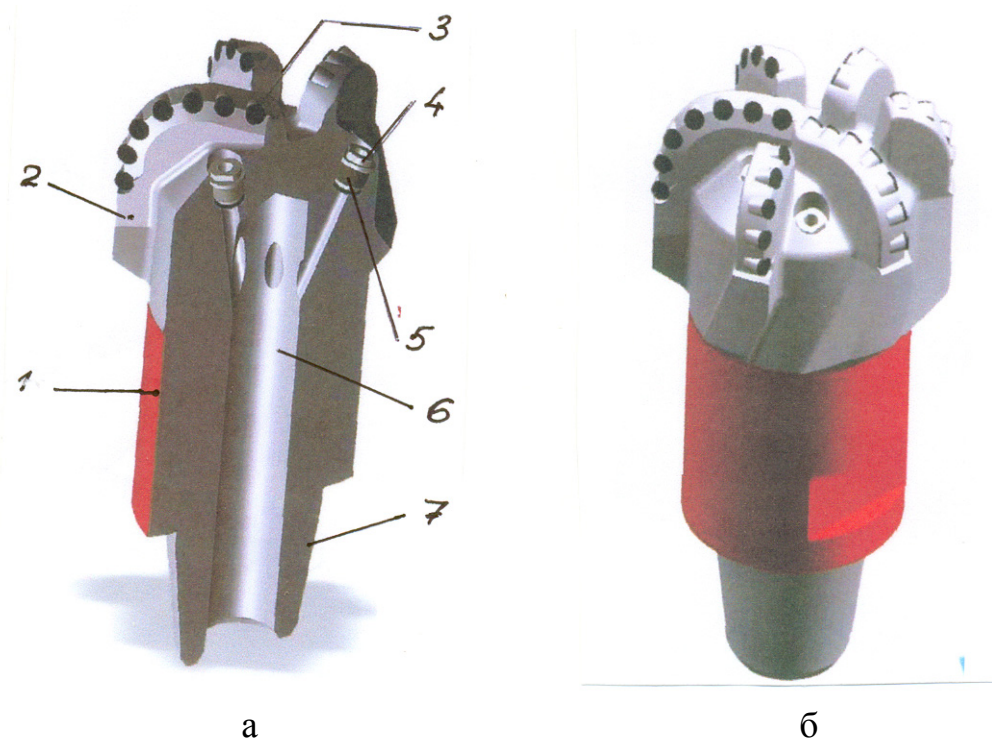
Устройство долота ДАП и его общий вид
